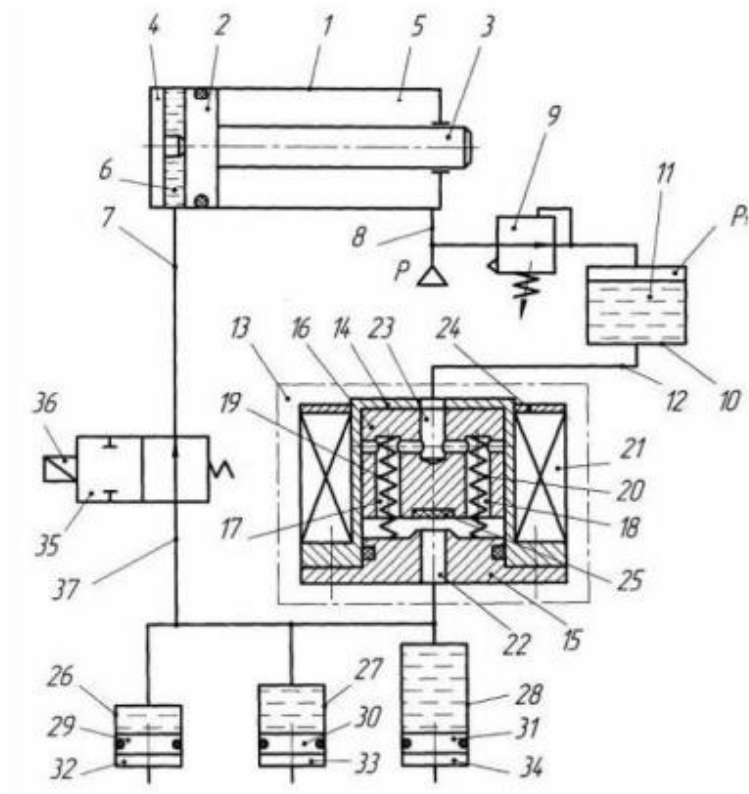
Позиційний привод з дозуючими пристроями: 1 – циліндр; 2 – поршень; 3 – шток; 4 - поршнева камера; 5 – камера штокова; 6 – поршнева камера; 7 – канал підвідний; 8 – підвідна магістраль; 9 – клапан редукційний; 10 – пневмогідравлічний бак; 11 – рідинна продукція; 12 -канал подачі рідини; 13 – розподільник; 14 – циліндр; 15 – корпус; 16 – якір; 17, 18 – робочі канали; 19, 20 – пружини; 21 – електромагнітна система; 22, 23 – гідравлічний канал; 25 – клапани; 26, 27, 28 – дозатори; 29, 30, 31 – поршні дозаторів; 32, 33, 34 – пневматичні ємності дозаторів; 35 – розподільники; 36 – електромагніти.
